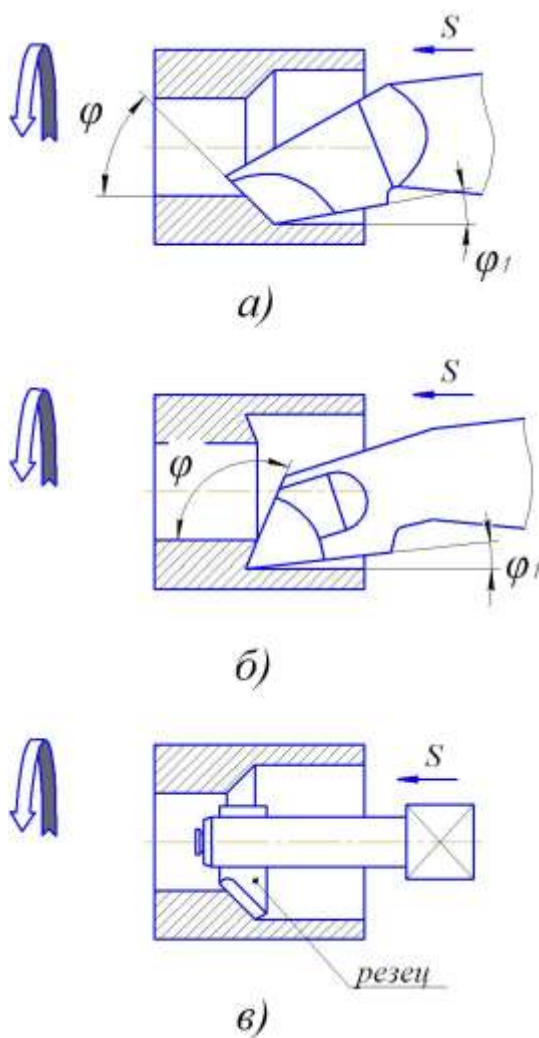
Растачивание: а) расточным проходным резцом; б) расточным упорно-проходным резцом; в) расточным проходным резцом на оправке (борштанге)
